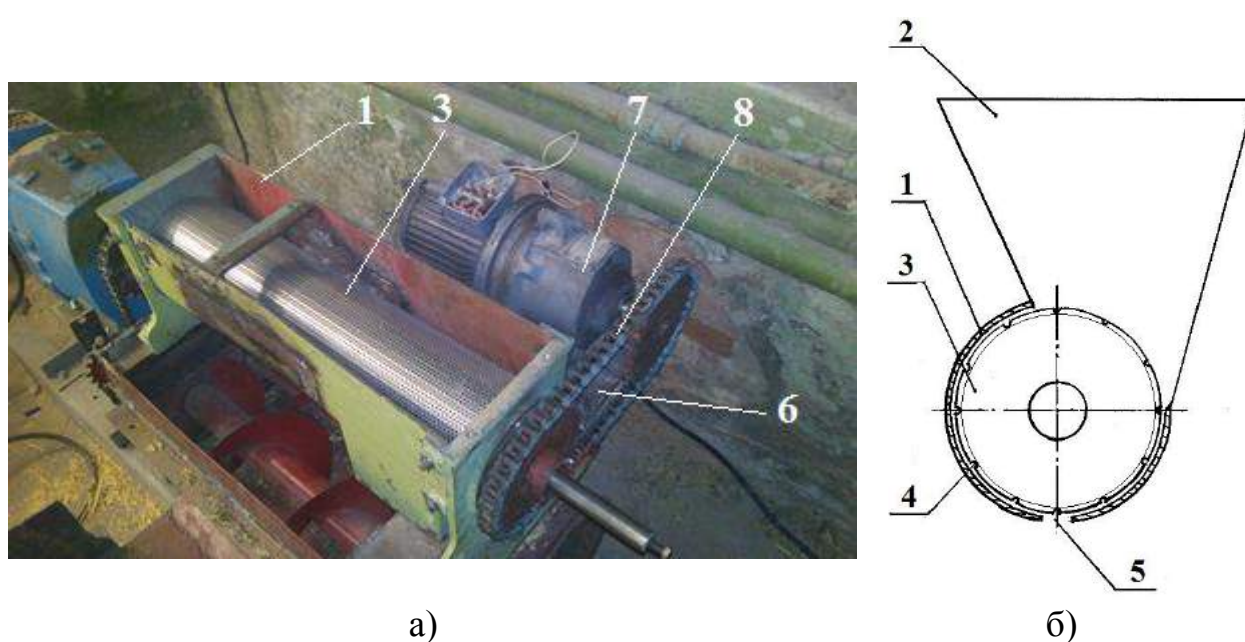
Дозатор для внесення пиловидного консерванту в масу корму: а – загальний вигляд; б – конструктивно-технологічна схема; 1 - корпус; 2 - бункер; 3 - барабан; 4 - коміркова поверхня; 5 - вивантажувальна щілина; 6 – рама; 7 - електроприводний мотор-редуктор; 8 - ланцюгова передача.
